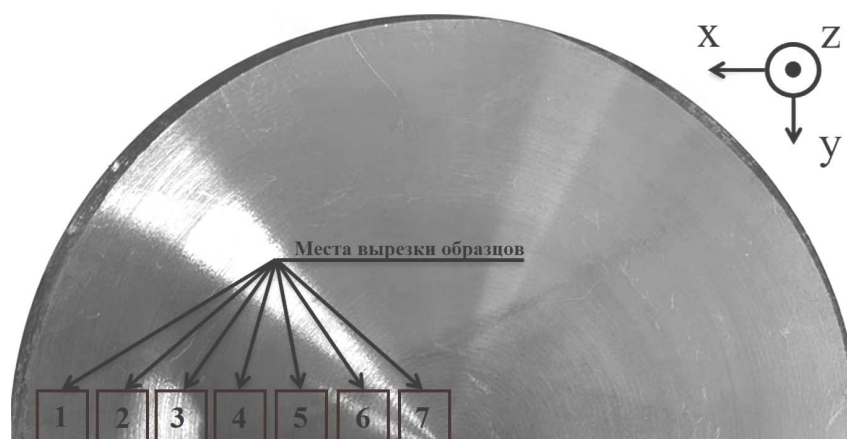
Заготовка из сплава ЭП741НП после ГИП
